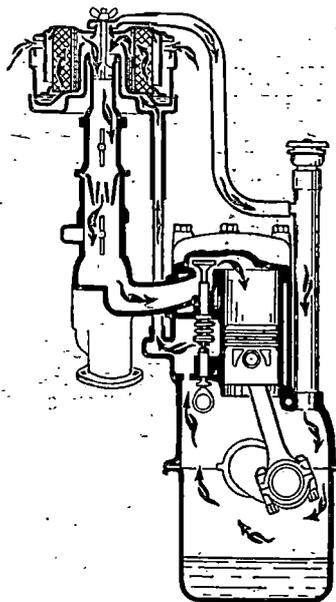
Схема вентиляции картера двигателя ГАЗ-51
